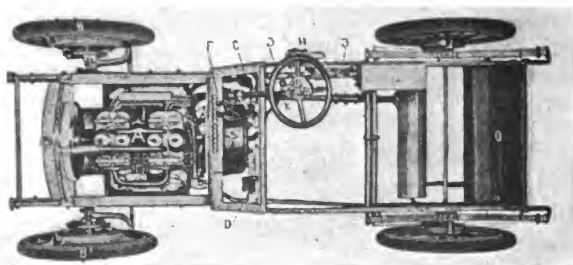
Draufsicht des Chassis des Lohner-Elektromobils.
